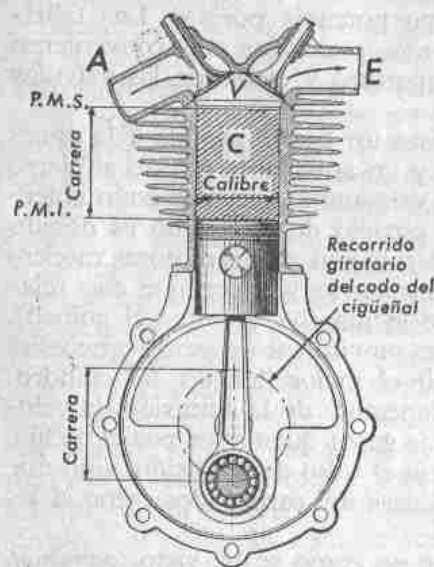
Dimensiones del motor, cilindrada y relación de compresión.
